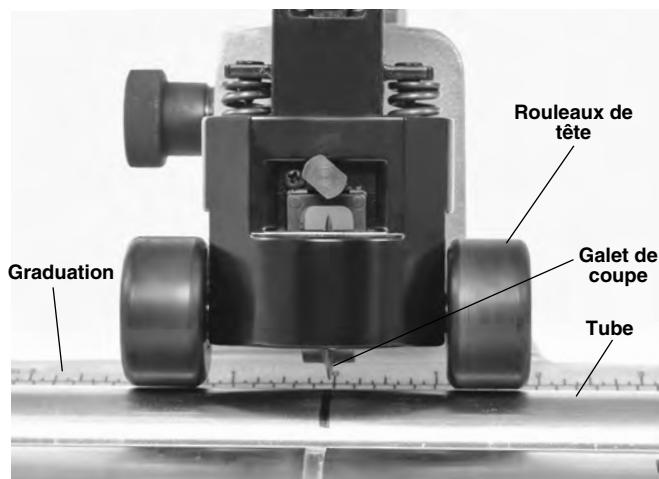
Rouleau de tête de coupe en contact avec le tube
